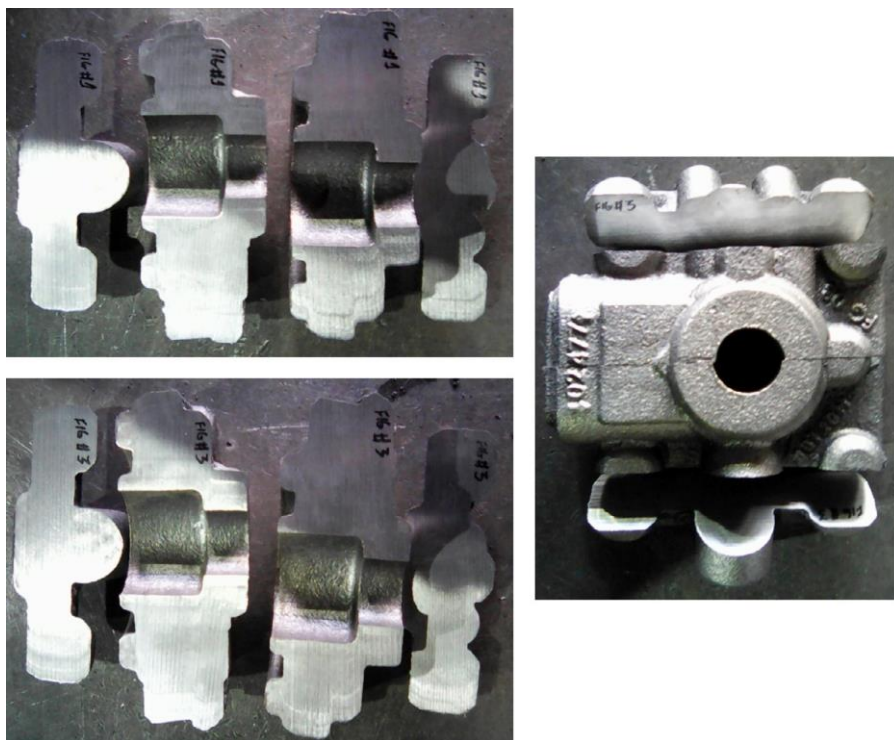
Качество отливки на примере крышки усилителя рулевого механизма: преимущество новой технологии очевидно.
